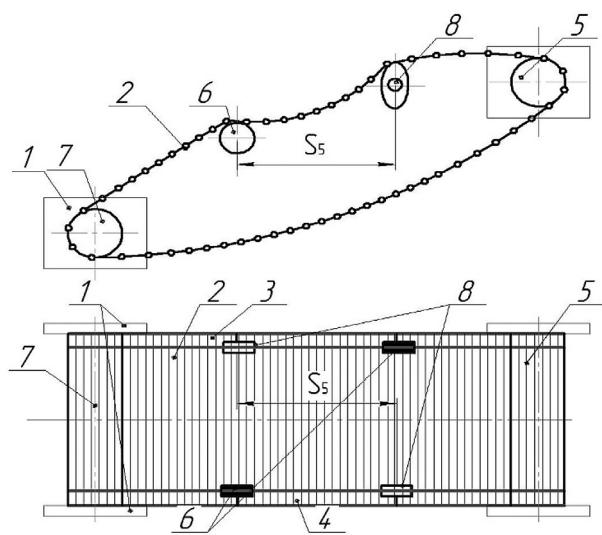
Схема пруткового элеватора с асимметричным расположением встряхивателей машины для уборки картофеля:
